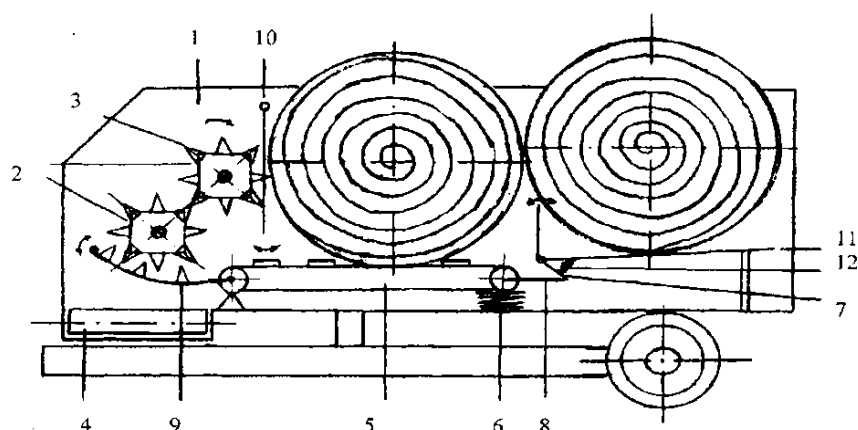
Конструктивно-технологическая раздатчика-измельчителя грубых кормов :1 - бункер; 2 - измельчающие барабаны; 3 - ножевые сегменты; 4 - поперечный (выгрузной) транспортер; 5 – продольный цепочно - планчатый транспортер; 6 - пружина; 7 - фиксатор рулона; 8 - рычаг; 9 - противорежущая дека; 10 - ограничительная решетка; 11 - фиксированная рама.
